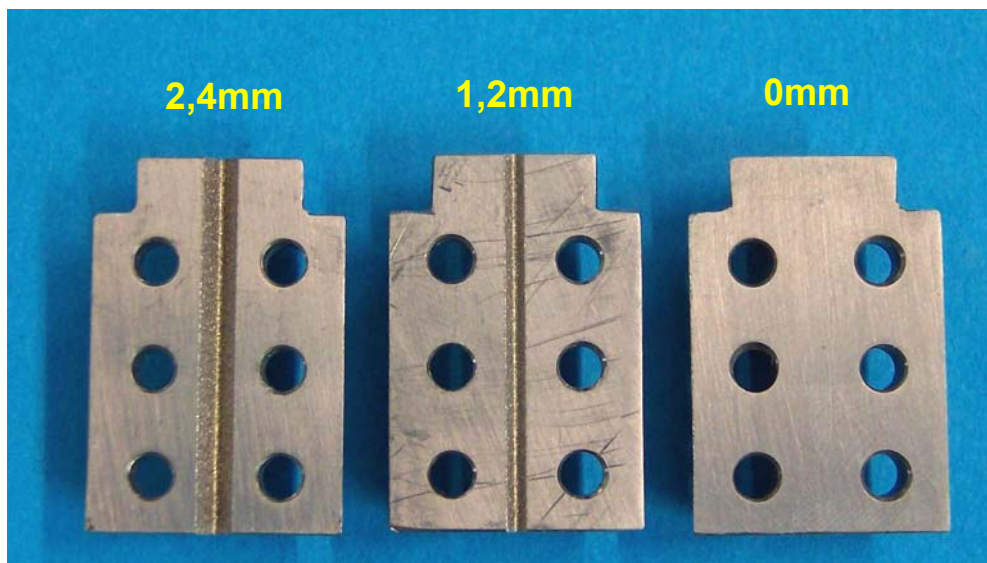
Platten für die Befestigung der Messproben am Halter
